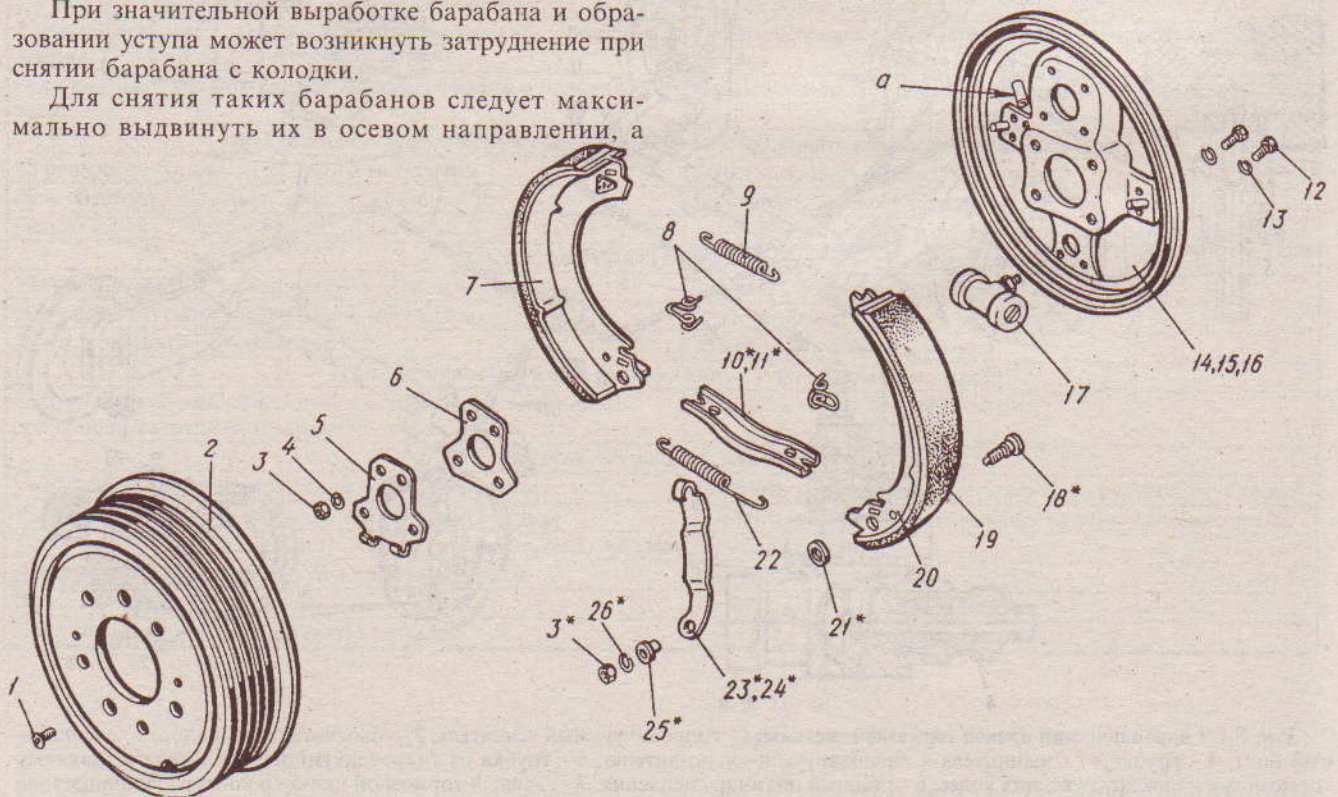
Тормоза передних и задних колес: 1 - винт М8; 2 - барабан тормозной; 3 - гайка М8; 4 - шайба 8Т; 5 - накладка опорной пластины; 6 - опора колодок тормоза; 7 - колодка тормоза в сборе левая; 8 - пружина прижимная; 9 - пружина стяжная колодок тормоза; 10 - планка распорная колодок тормоза правая (метка - 3 риски); 11 - планка распорная колодок тормоза левая (метка - 2 риски); 12 - болт М6; 13 - шайба 6Л; 14 - щит переднего тормоза; 15 - щит заднего тормоза правый; 16 - щит заднего тормоза левый; 17 - цилиндр колесный тормоза; 18 - винт регулировочный разжимного механизма; 19 - накладка фрикционная; 20 - колодка тормоза правая; 21 - шайба 8; 22 - пружина стяжная; 23 - рычаг разжимной ручного тормоза правый; 24 - рычаг разжимной ручного тормоза левый; 25 - втулка; 26 - шайба 8Л
